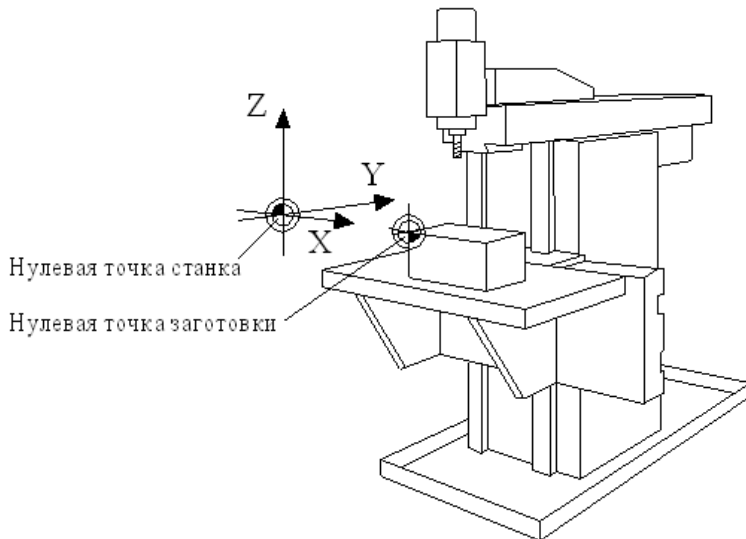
Нулевые точки станка и заготовки при фрезерной обработке на станке с ЧПУ
